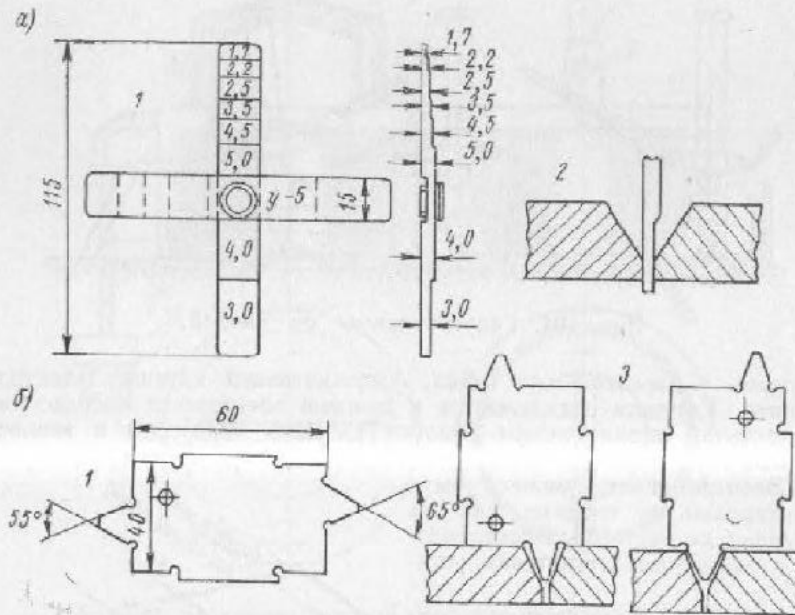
Шаблоны для проверки зазоров и углов разделки: а — шаблон-цип для измерения зазоров; б — предельный шаблон для проверки угла разделки кромок.
